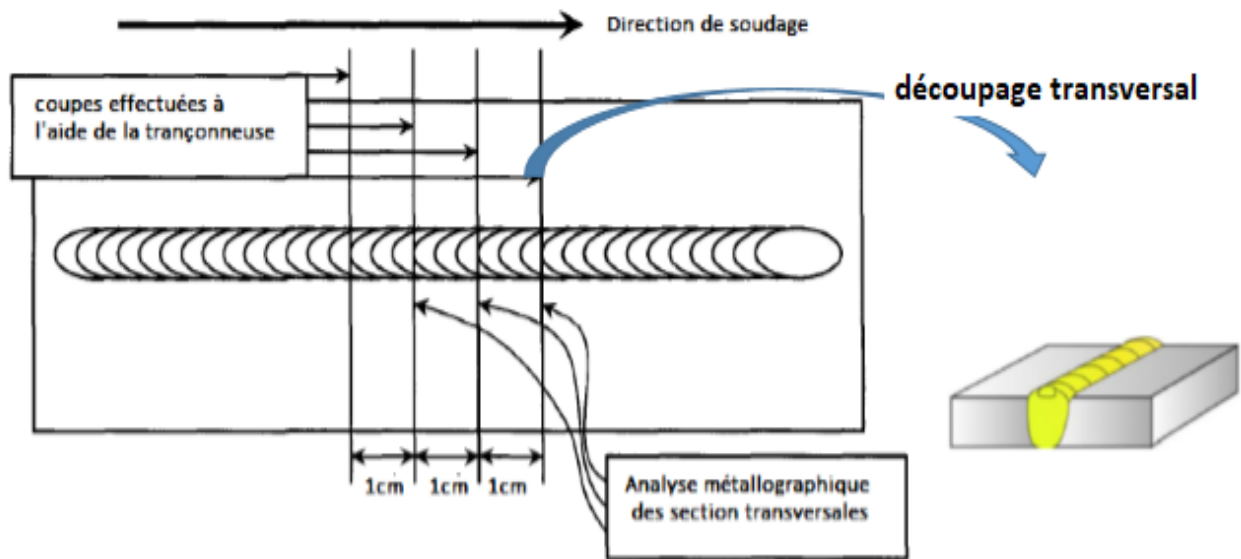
Schéma de découpage des échantillons de soudure
